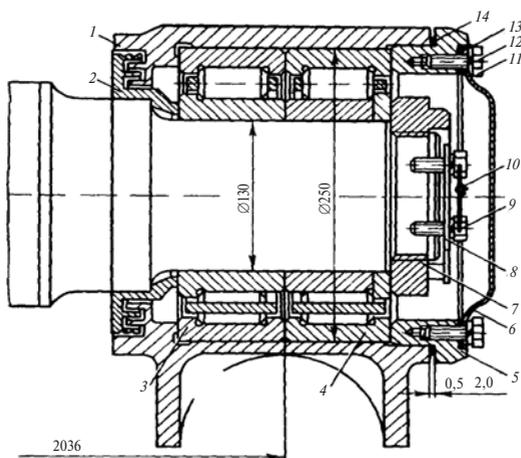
Букса пассажирского вагона с двумя цилиндрическими подшипниками с торцевым креплением корончатой гайкой:
